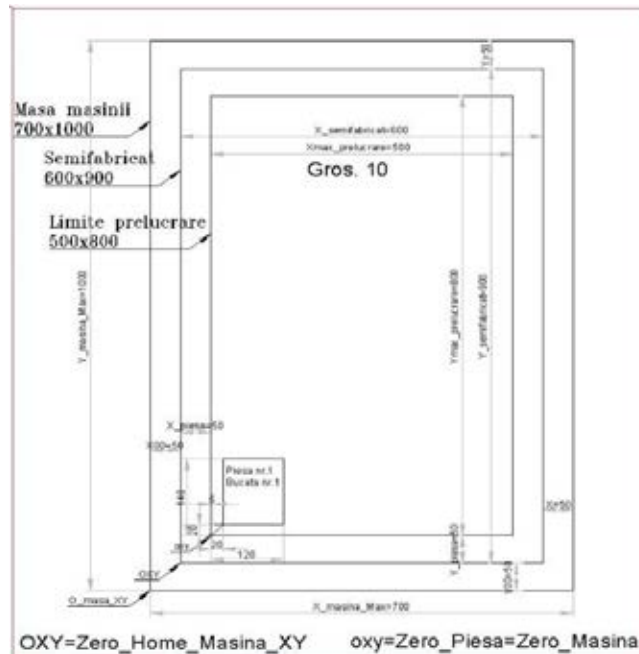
Poziționarea piesei Nr.1 Buc. Nr.1 „PLACA 100 x120 x10 Poz.11” pe semifabricat de dimensiuni 600x900 și pe masa mașinii CNC 6090 de dimensiuni 700x1000
